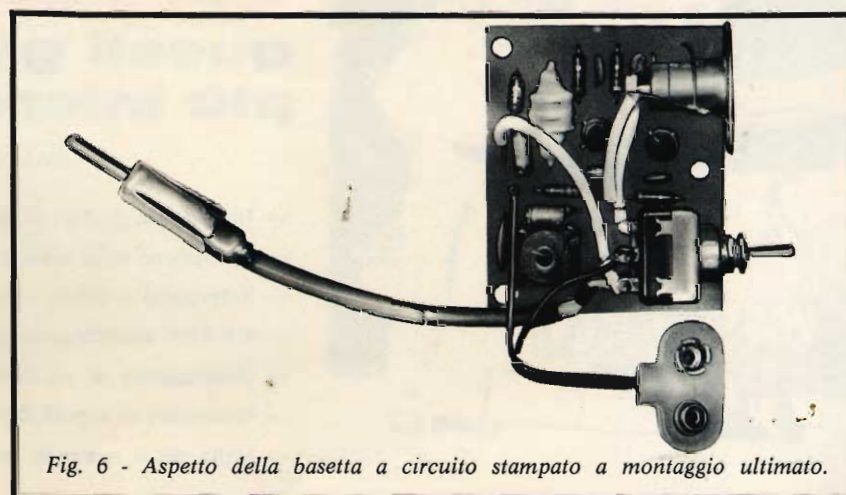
Aspetto della basetta a circuito stampato a montaggio ultimato.
